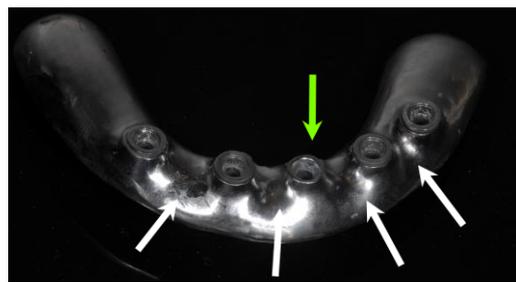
Bandeja o parte baja que muestra emergente central colado con la bandeja y cuatro laterales soldados
